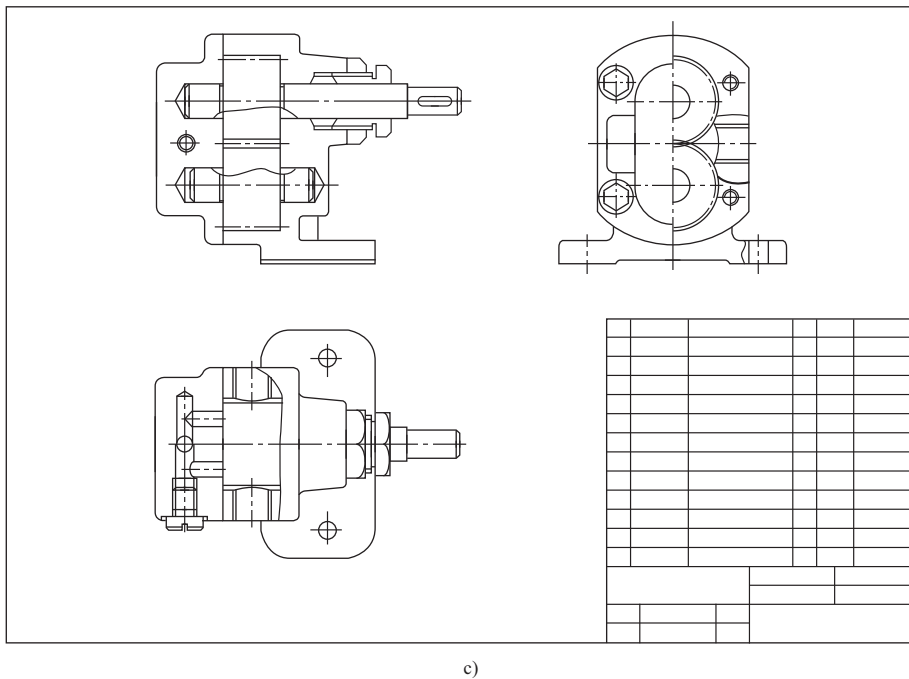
齿轮油泵装配图的绘图步骤 (续)
